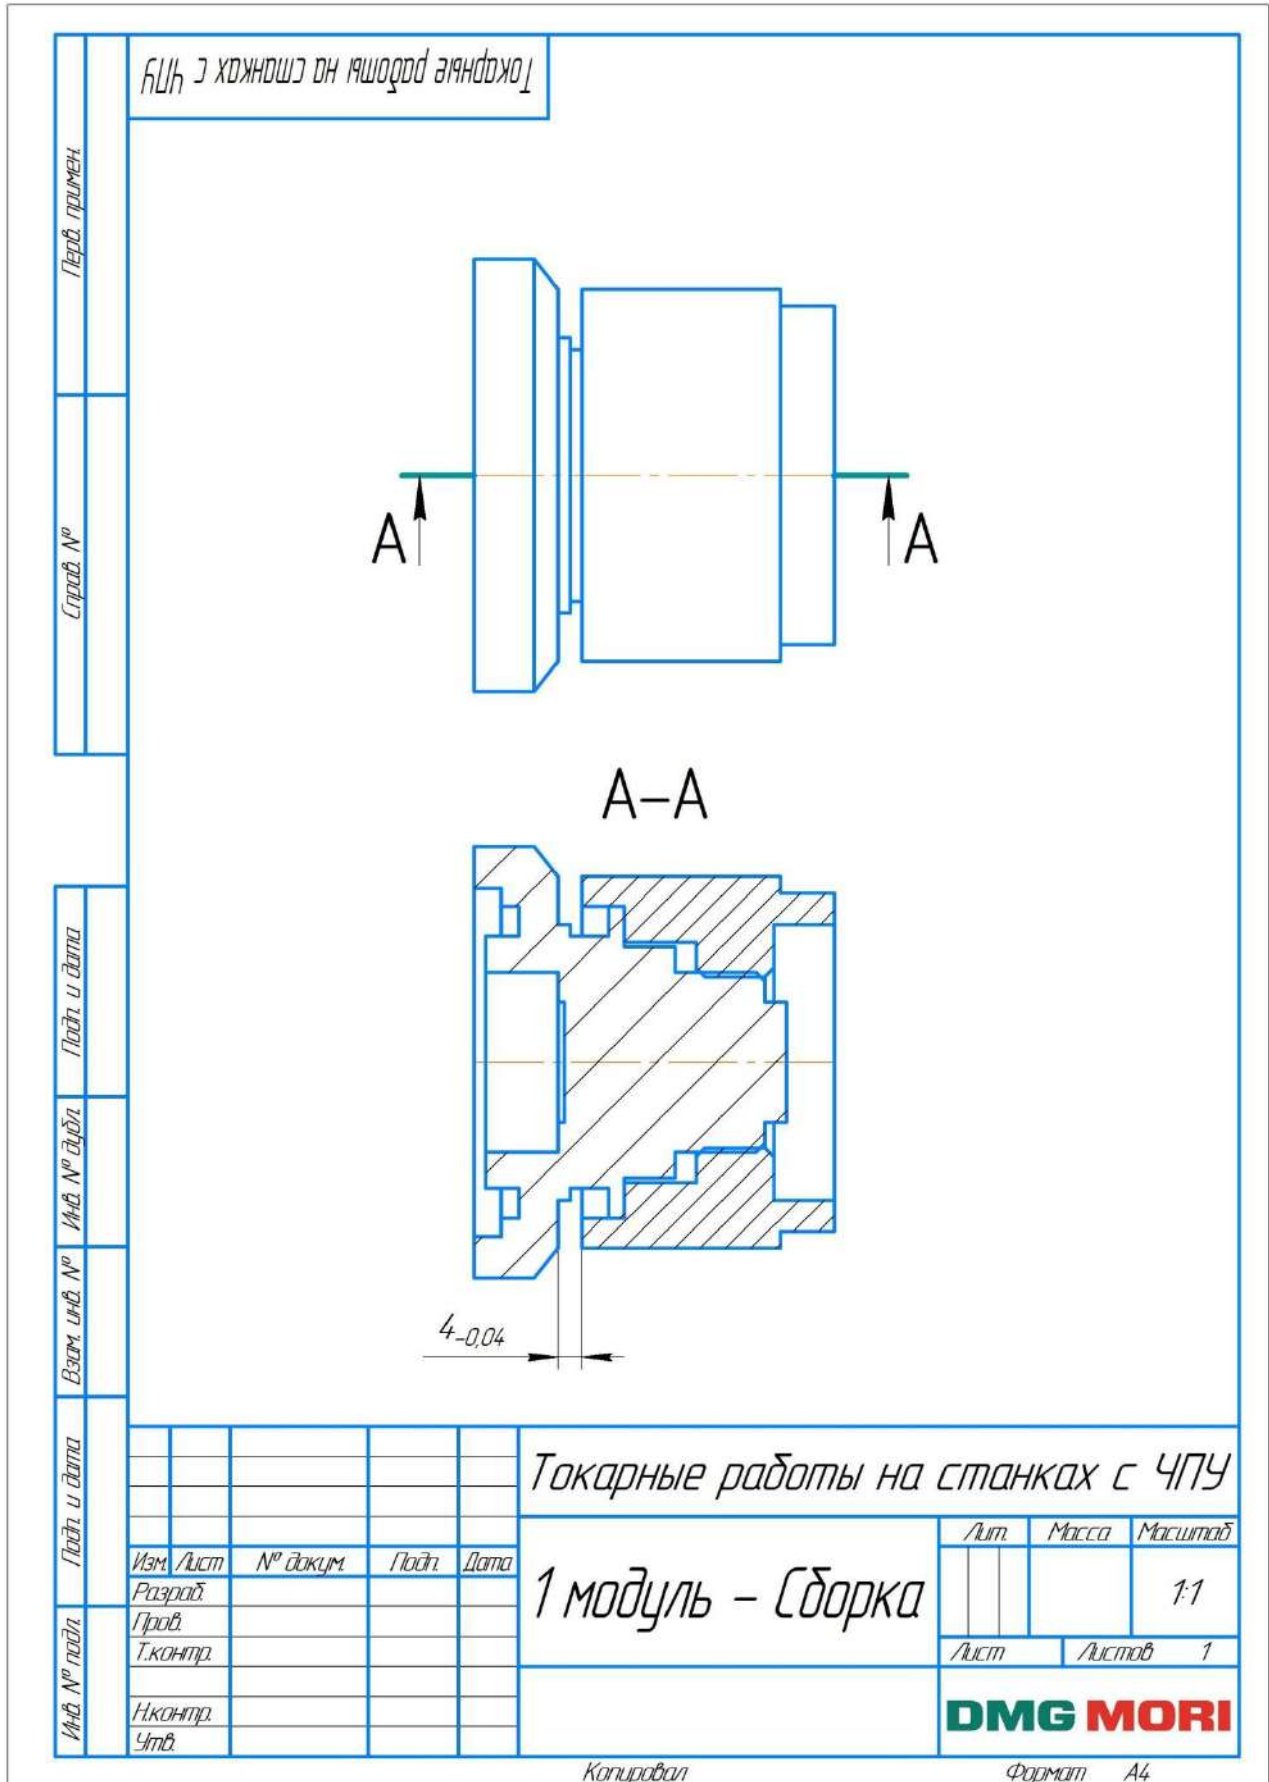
Модуль 1 Сборочный чертеж Токарные работы на станках с ЧПУ
